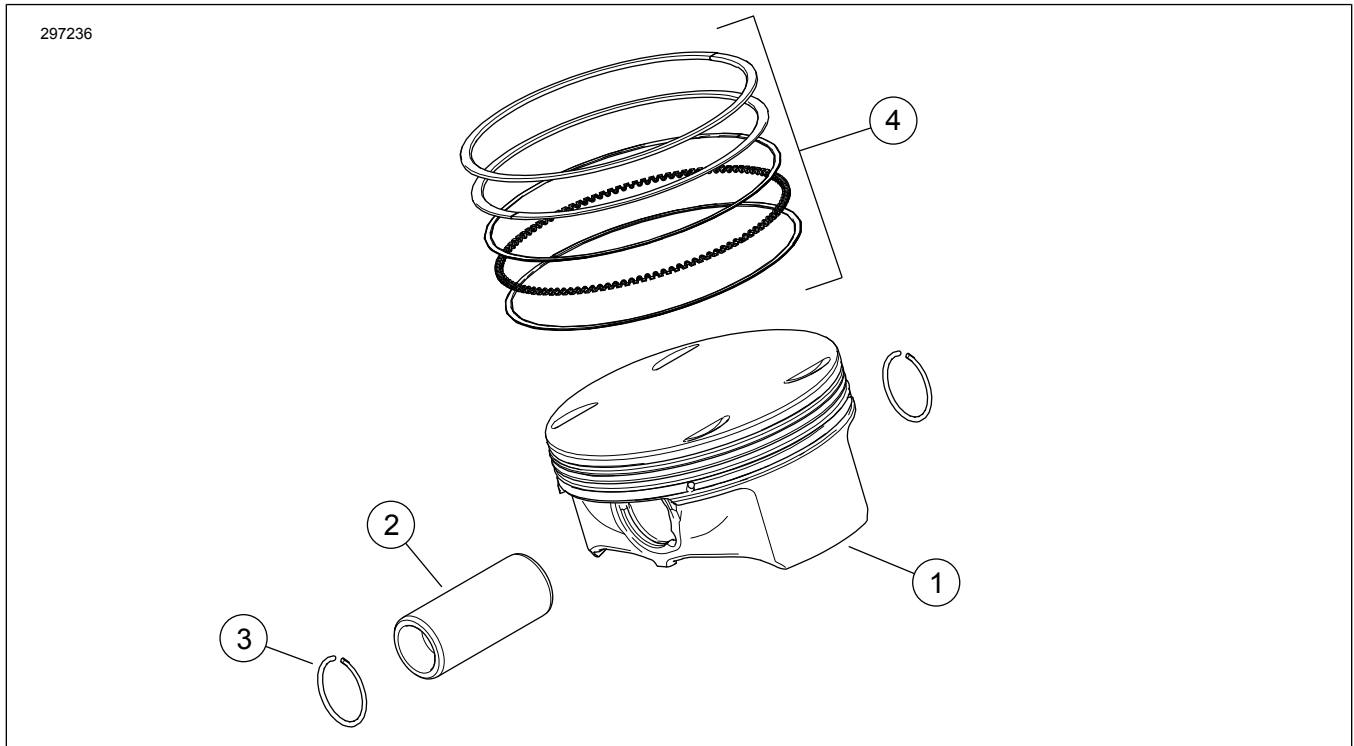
Pièces de rechange : Kits piston Screamin' Eagle Big Bore 135
